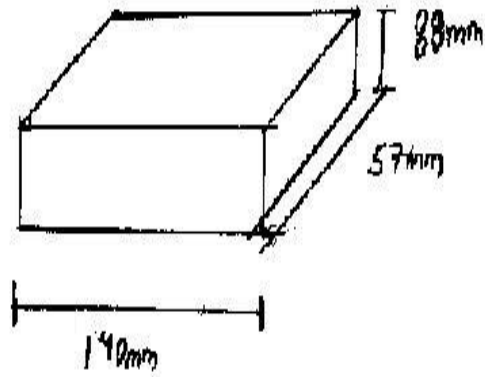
Boceto del diseño final del calentador con celdas de combustible, detallando piezas que serán utilizadas para su fabricación, parte 1.
